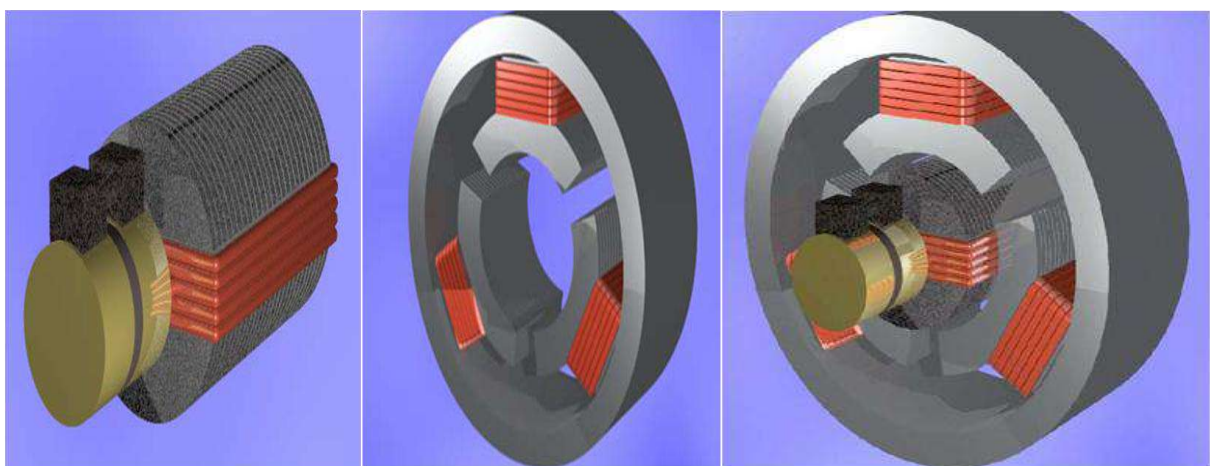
b. La structure des machines à induit fixe et inducteur tournant
